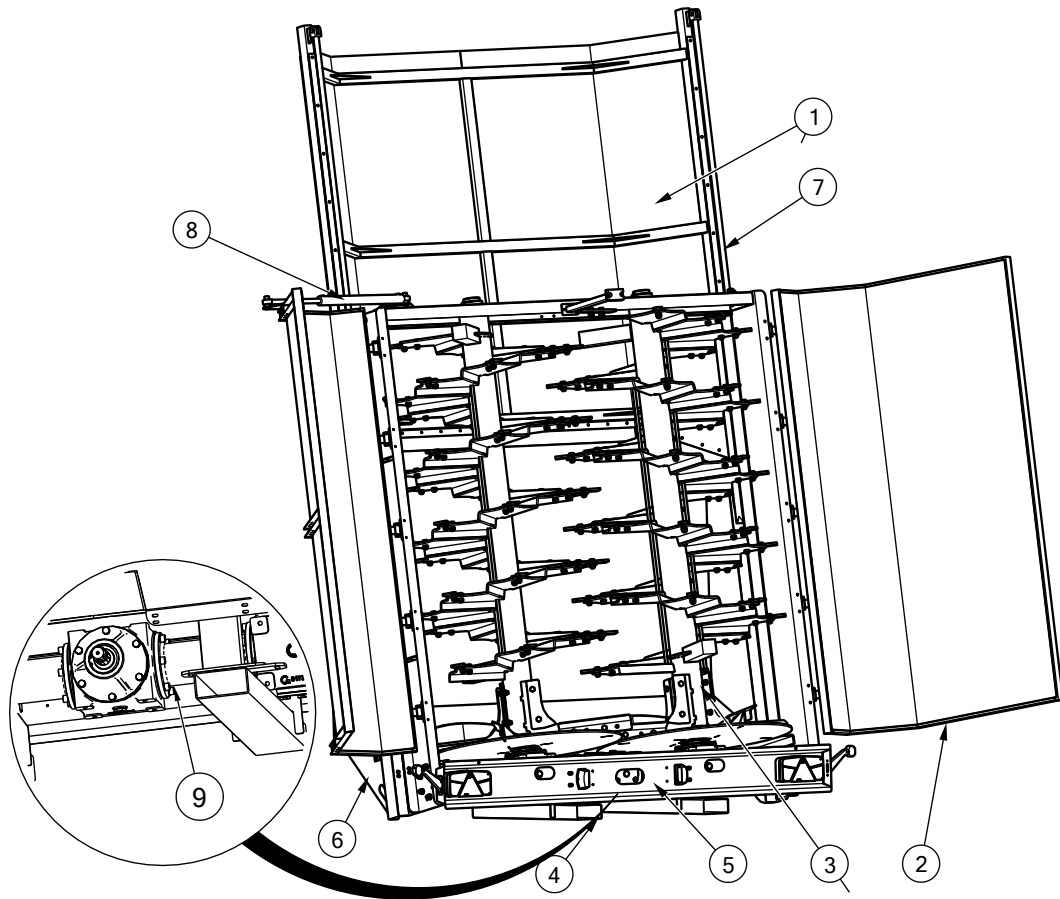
Вертикальный 2-роторный адаптер. (1) заслонка (2), дефлектор, (3) рабочий шнек, (4) вилочная опора, (5) балка освещения, (6) основная рама, (7) привод заслонки, (8) привод дефлектора, (9) редуктор
